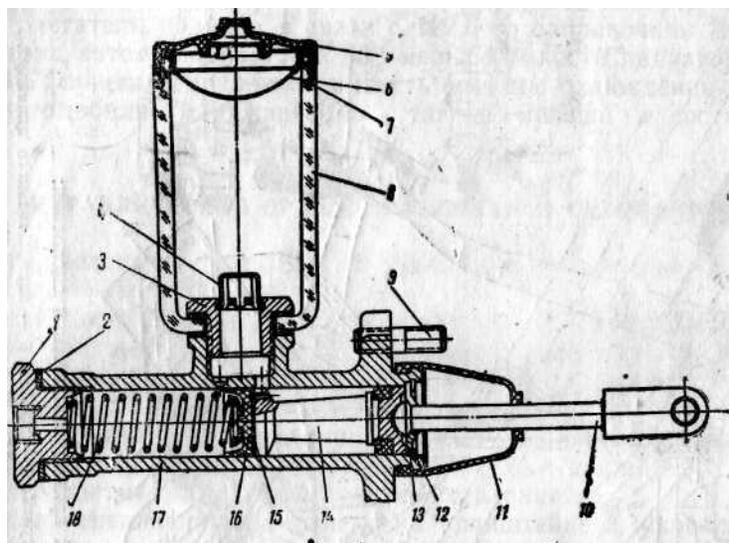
Главный цилиндр гидропривода выключения сцепления:
